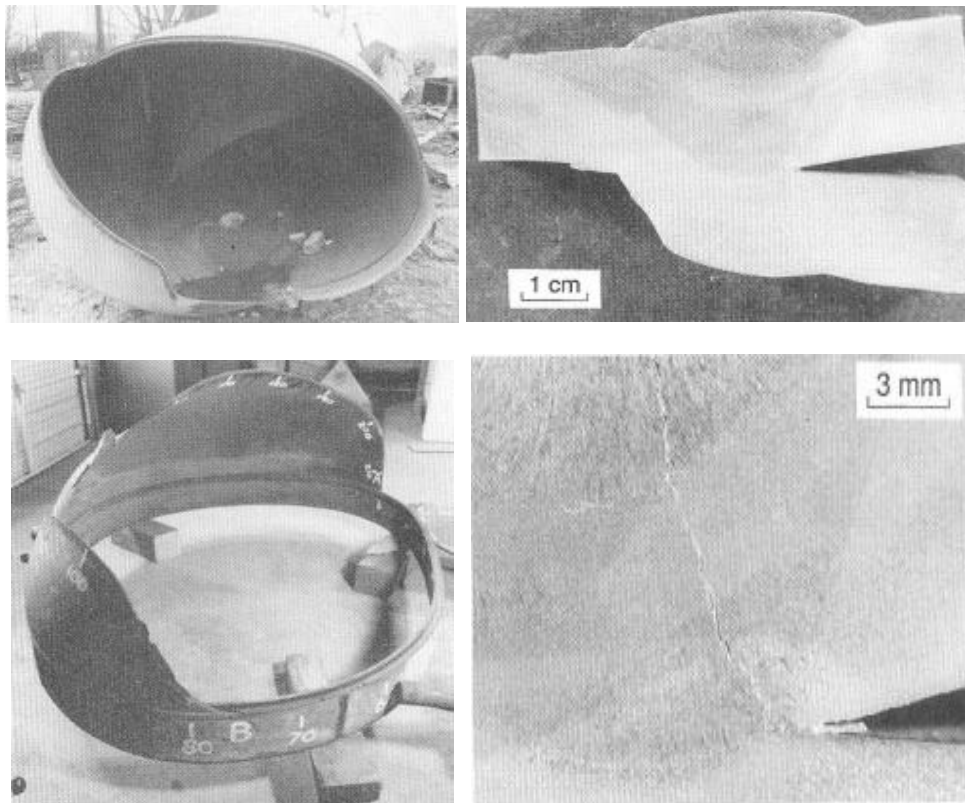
Tanque de propano que explodiu devido a uma trinca que se originou no cordão de solda.
